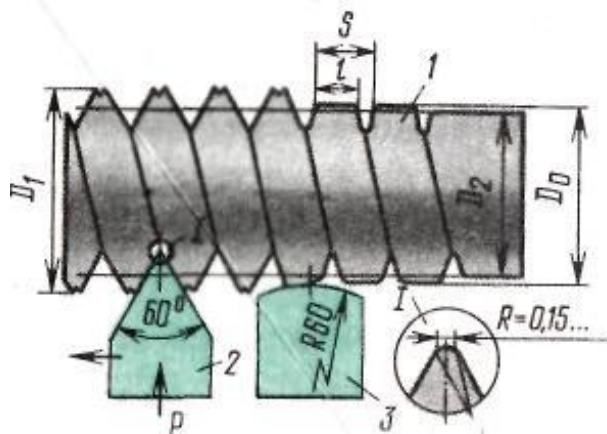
Схема восстановления детали электромеханической обработкой: 1 — деталь; 2 — высаживающий инструмент; 3 — сглаживающий инструмент.
